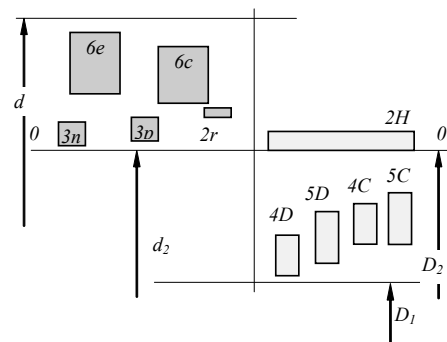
Розташування полів допусків різьб із натягом
